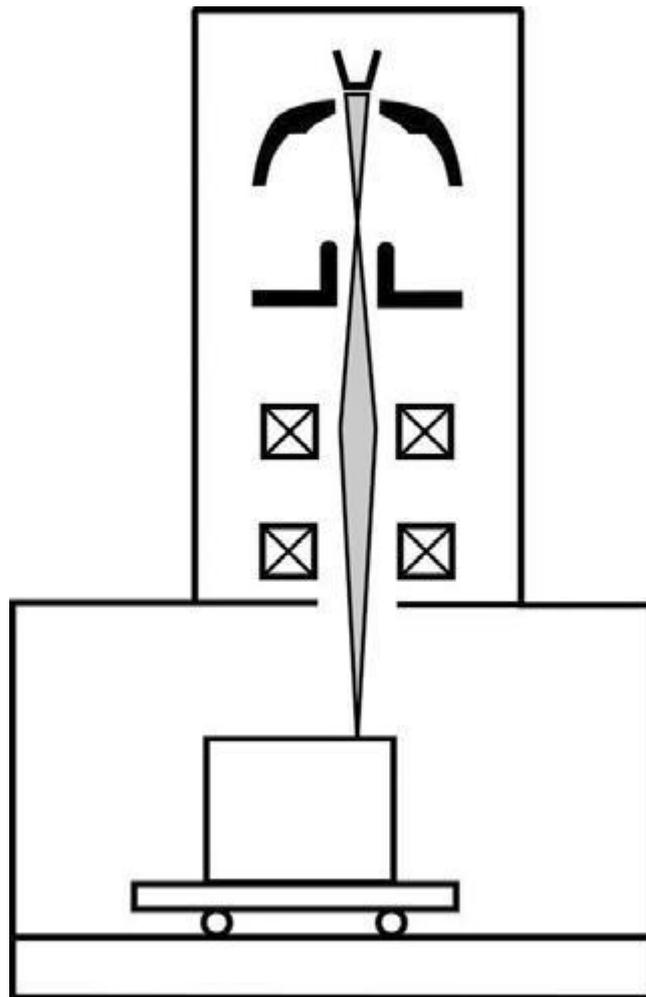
Principe du soudage par faisceau d'électrons [3].
